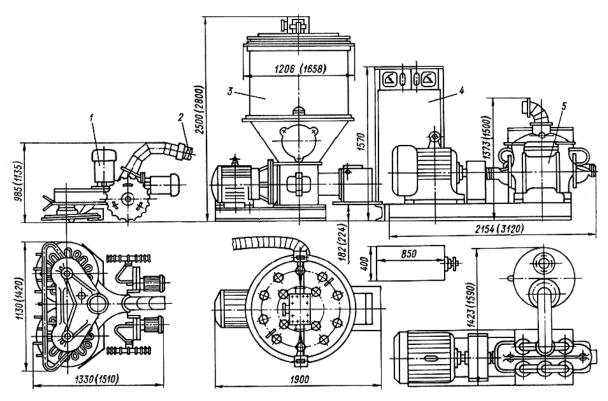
Заборное устройство пневматического разгрузчика всасывающего типа
